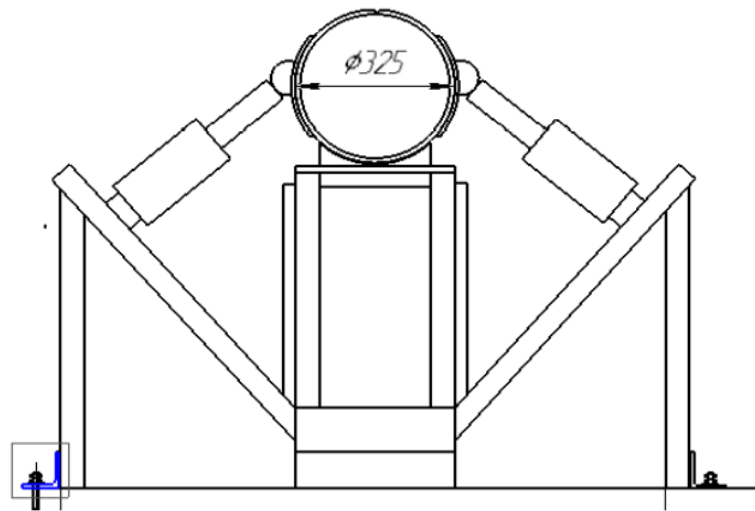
Установка для зварювання поздовжніх швів
